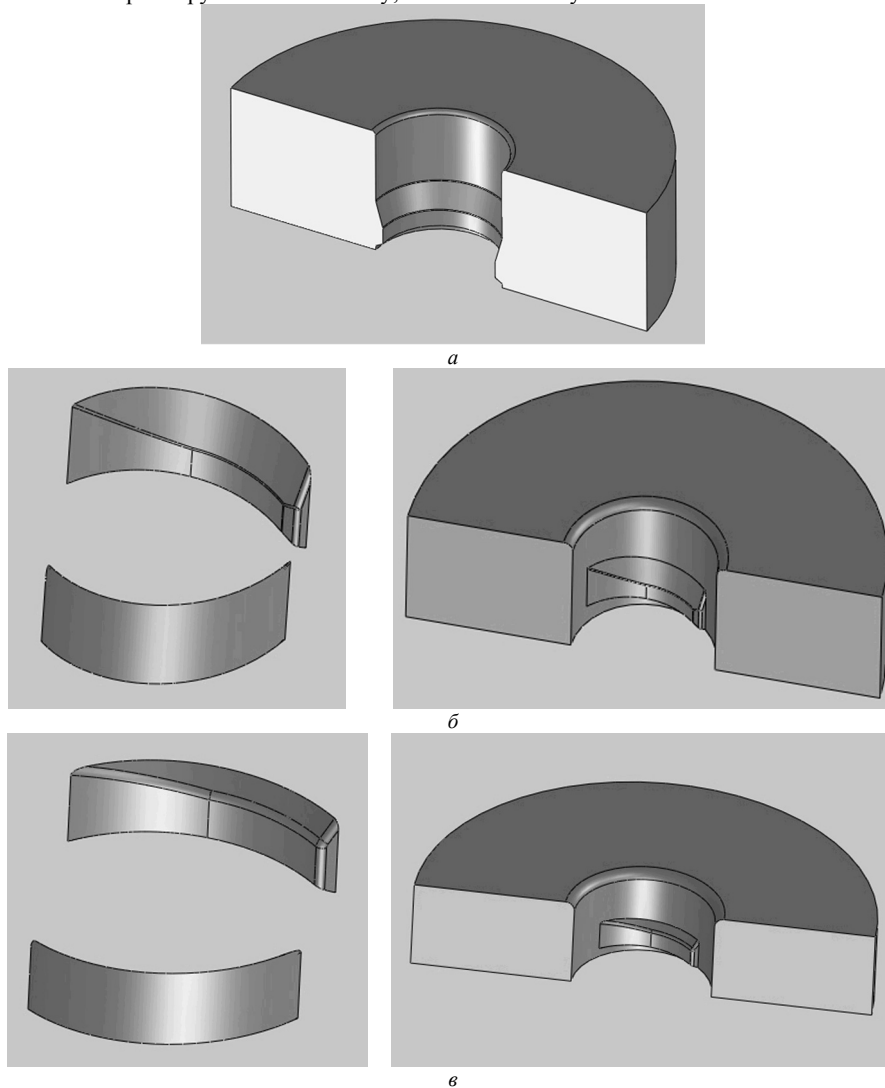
Геометрія робочих кромки матриць: *a* - матриця з циліндричною робочою кромкою; *б*-матриця з гвинтовою двохзахідною робочою кромкою зі спеціальним профілем з кутом робочої конічної частини $\alpha = 15^\circ$; *в*-матриця з гвинтовою двохзахідною робочою кромкою зі спеціальним профілем з кутом робочої конічної частини $\alpha = 45^\circ$
